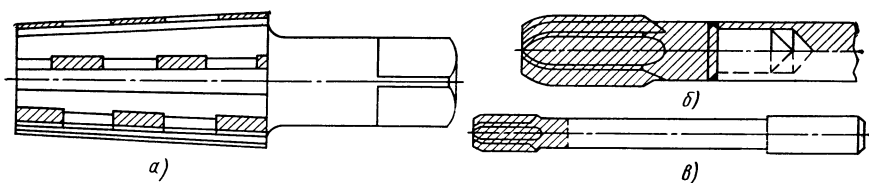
Развертки, оснащенные пластинками из твердого сплава:
